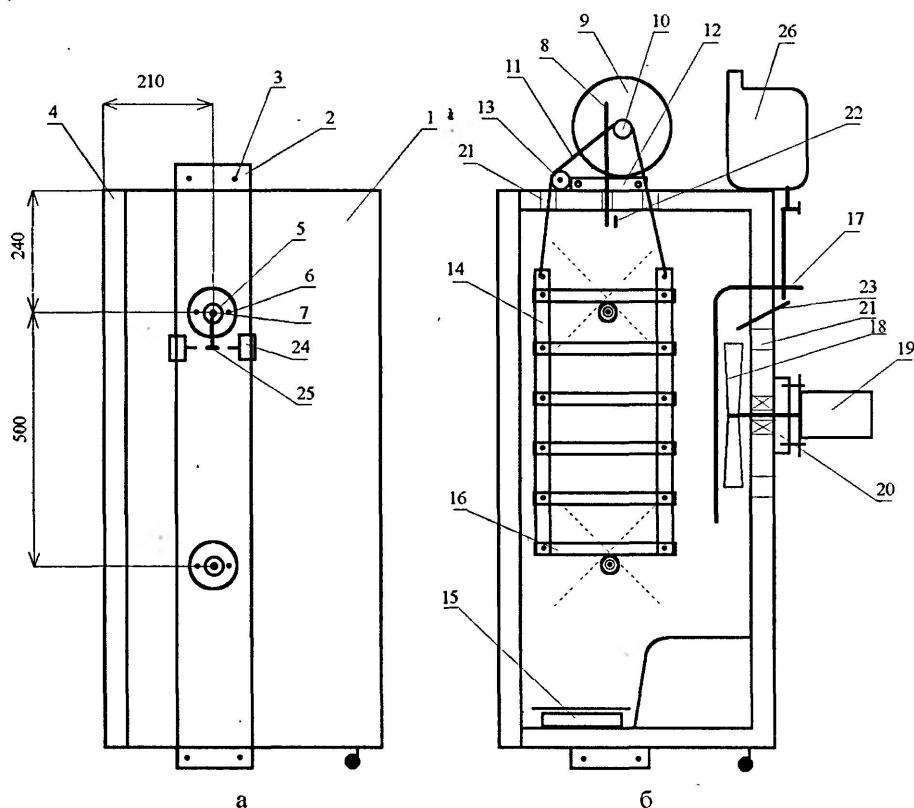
Корпус инкубатора из холодильника. Общий вид
